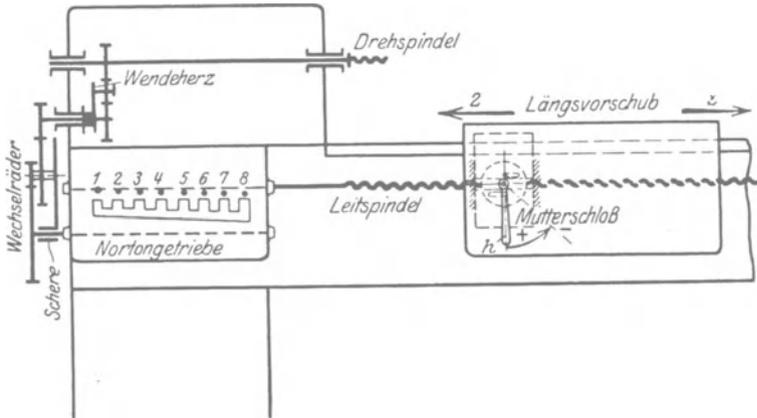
Längszug mit Leitspindel für eine Gewindedrehbank.
